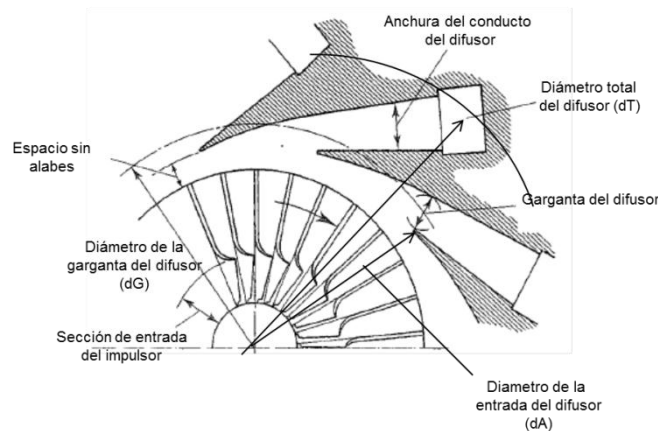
Sección transversal de un compresor (rotor y estator) [1].
